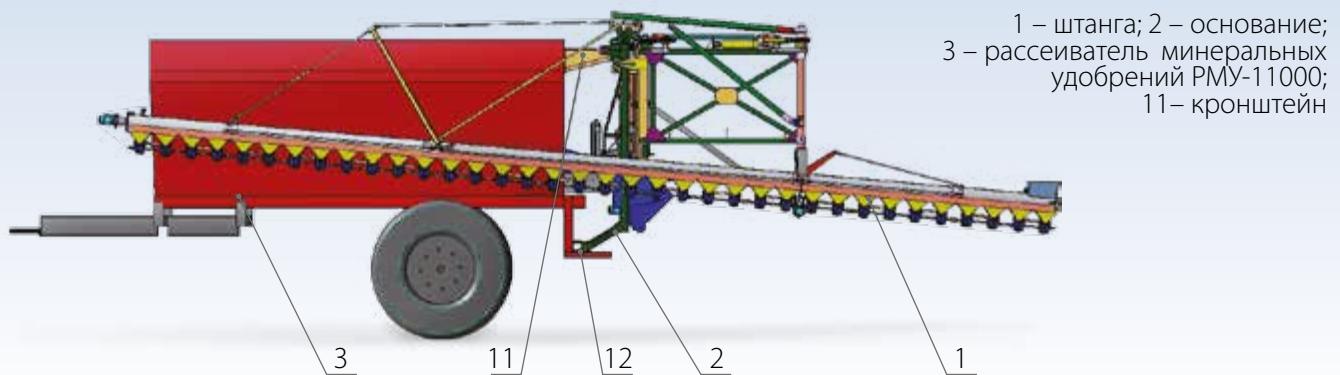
Схема распределителя штангового навешенного на рассеиватель РМУ-11000 (в транспортном положении)
